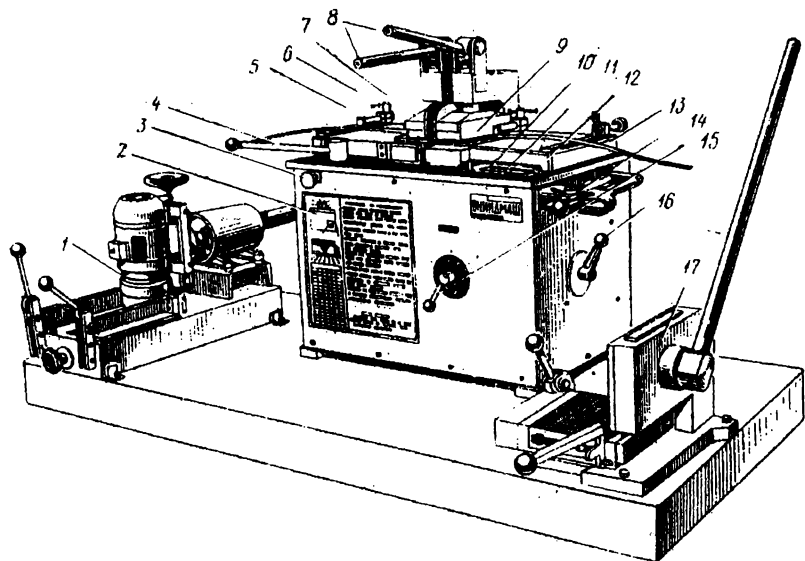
Агрегат АСЛП18 для стыковой сварки делительных ленточных пил
